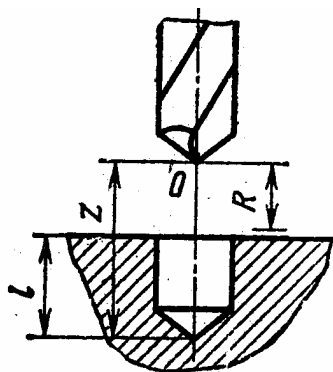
Сверление отверстия в заготовке на станке с ЧПУ
